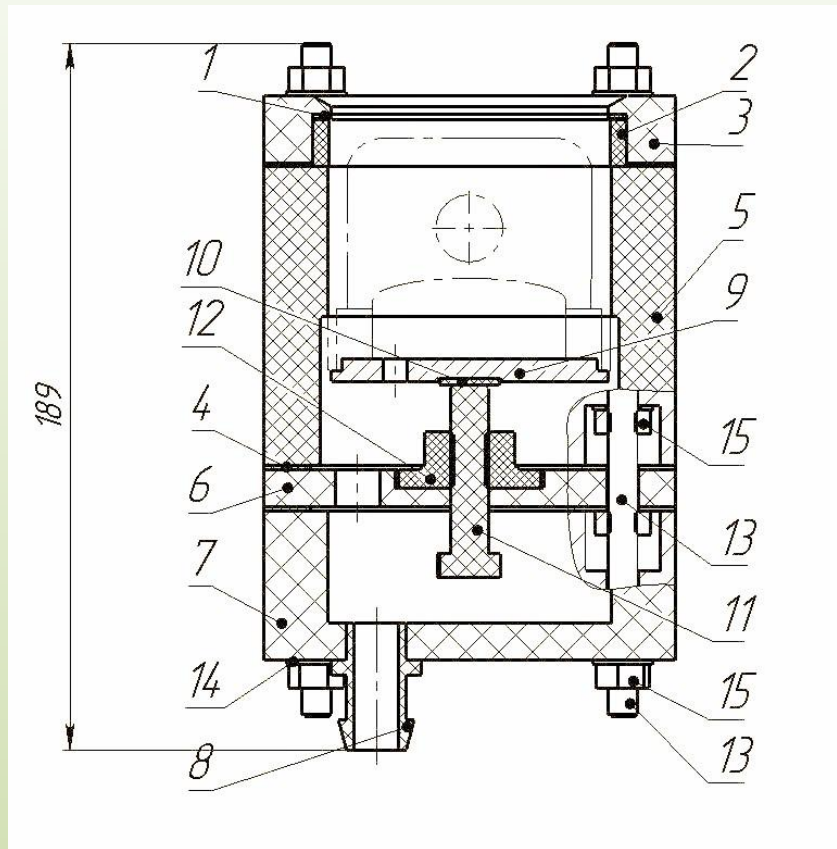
Приспособление для обработки поршня двигателя РМЗ-550 методом МДО, в разрезе: 1 – упрочняемый поршень; 2 – главный уплотнительный элемент; 3 – центрирующая втулка; 4 – крышка; 5 – уплотнительный элемент; 6 – корпус; 7 – промежуточная крышка; 8 – корпусная крышка; 9 – штуцер; 10 – токоподводящая пластина; 11 – изолирующая шайба; 12 – натяжительная втулка; 13 – болт; 14 – шайба; 15 – гайка; 16 – шпилька
